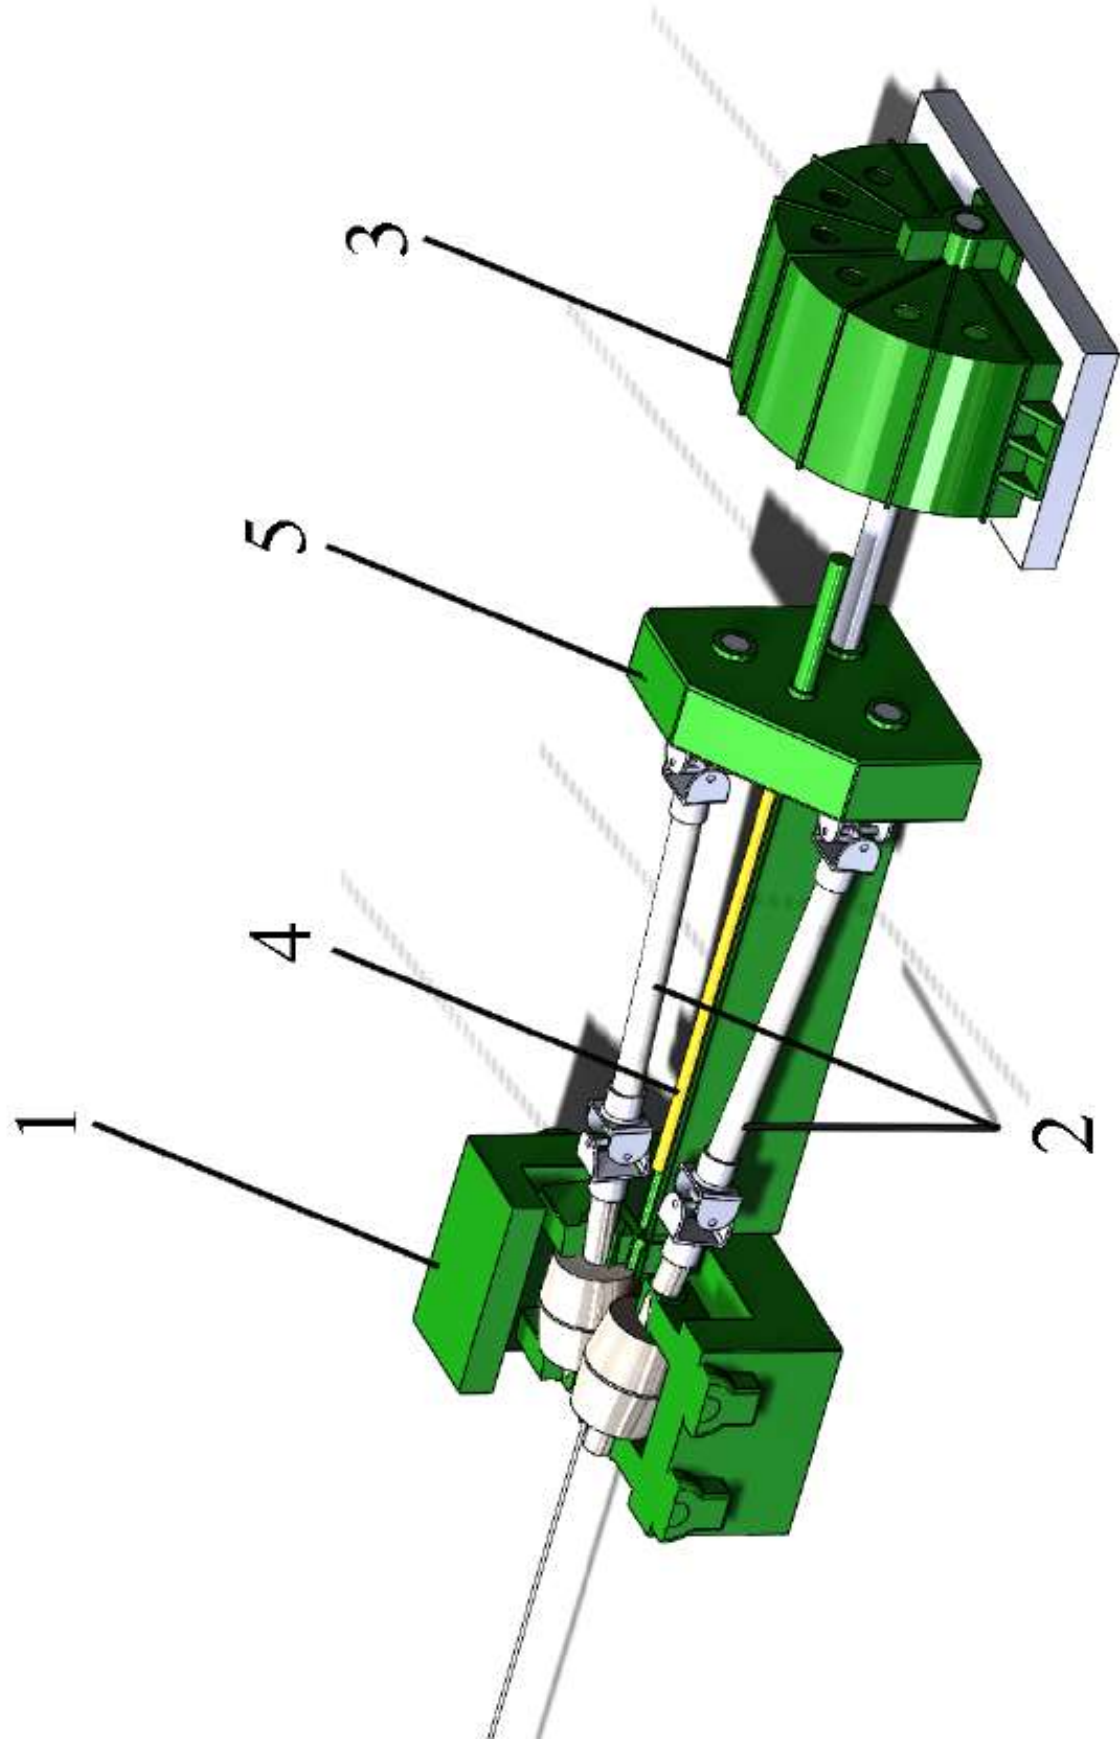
Прошивной стан: 1 – прокатная клет; 2 – шпиндели; 3 – двигатель; 4 – трубная заготовка; 5 – шестеренная клет
